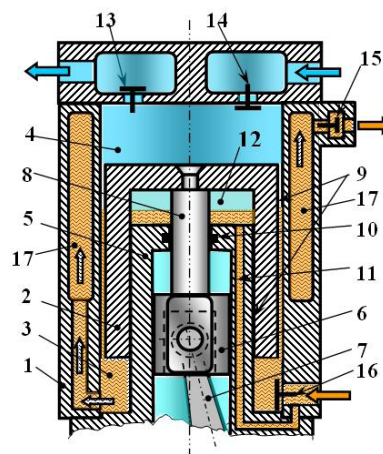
Схема ПГЭМОД с П-образным поршнем:
